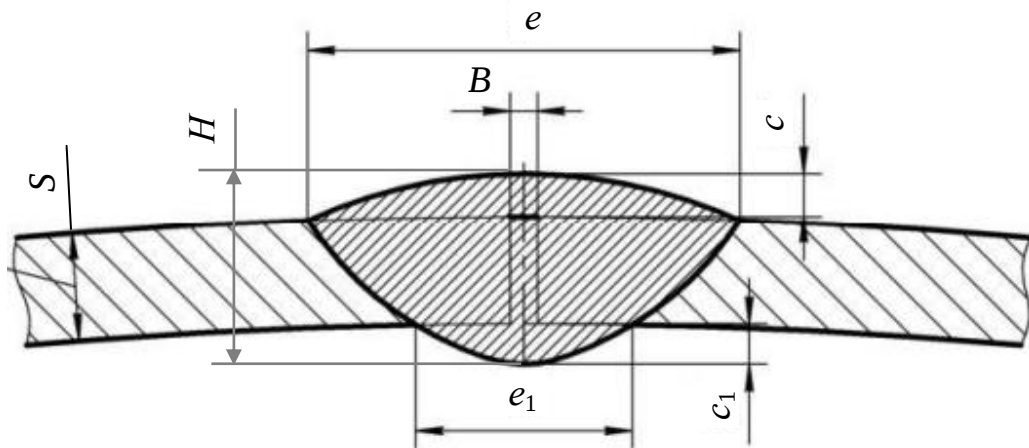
Схема до розрахунку параметрів автоматичного зварювання під шаром флюсу
